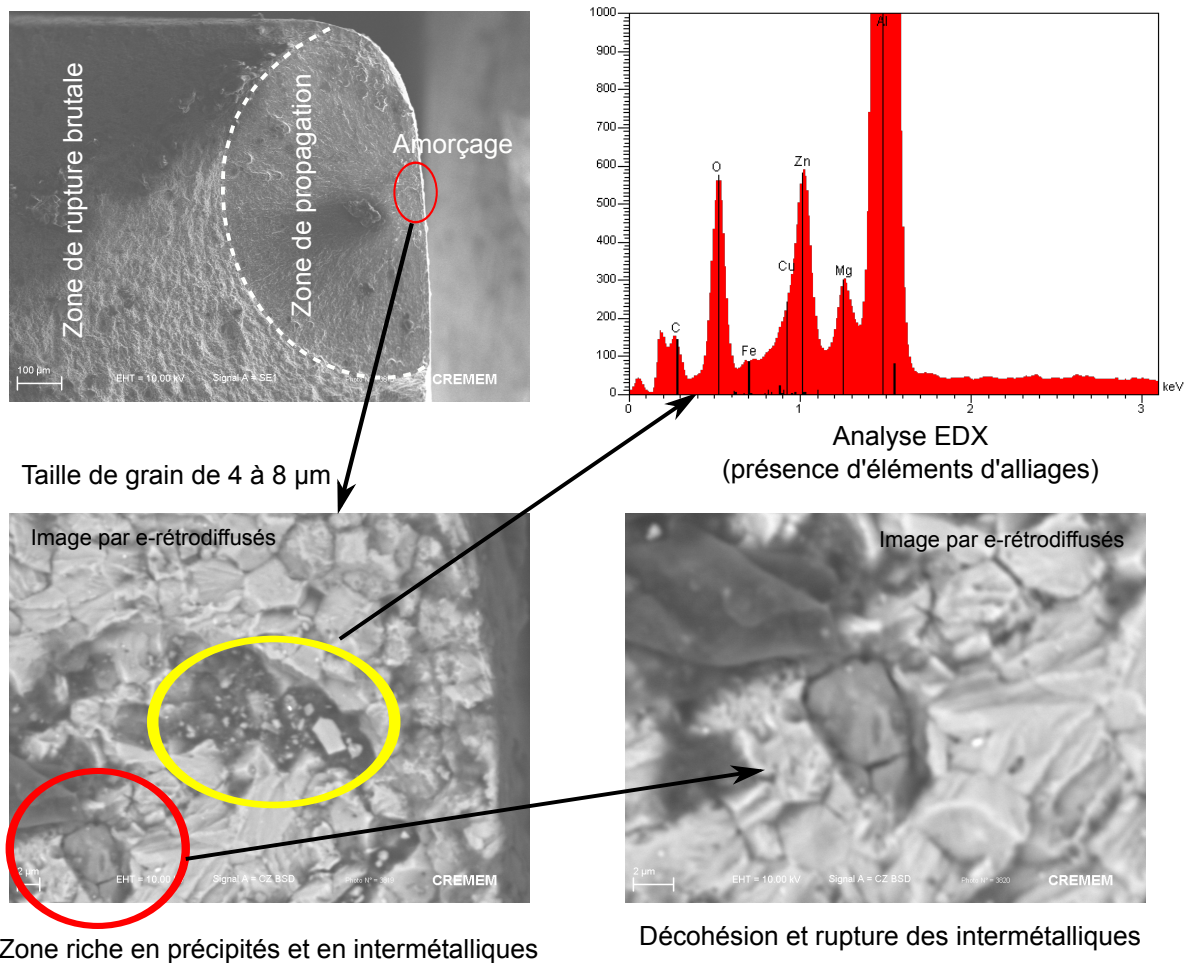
Observation de la zone d’amorçage de fissure de fatigue dans le noyau des joints soudés par FSW (ici en alliage 7449-T79)
